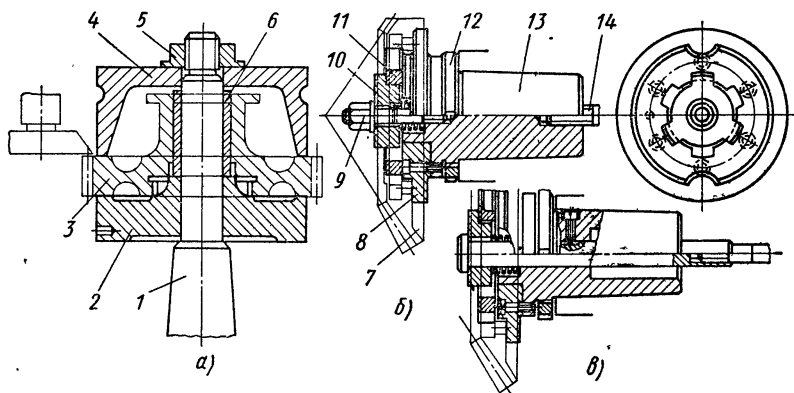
Типовые приспособления к зубострогальным и долбежным станкам
